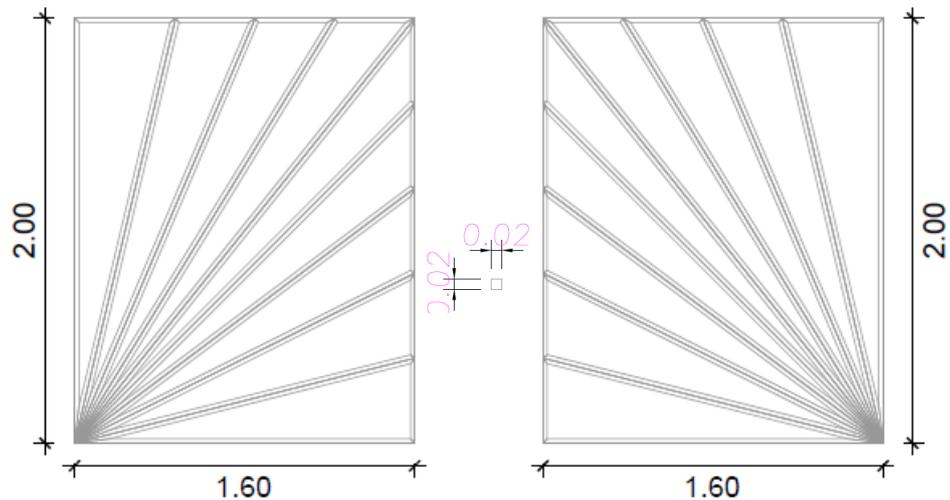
Vista frontal armado de puerta abanico con tubo cuadrado
